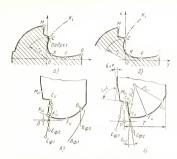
Форма профиля фрезы и канавки сверла при различных значениях параметров установки фрезы
